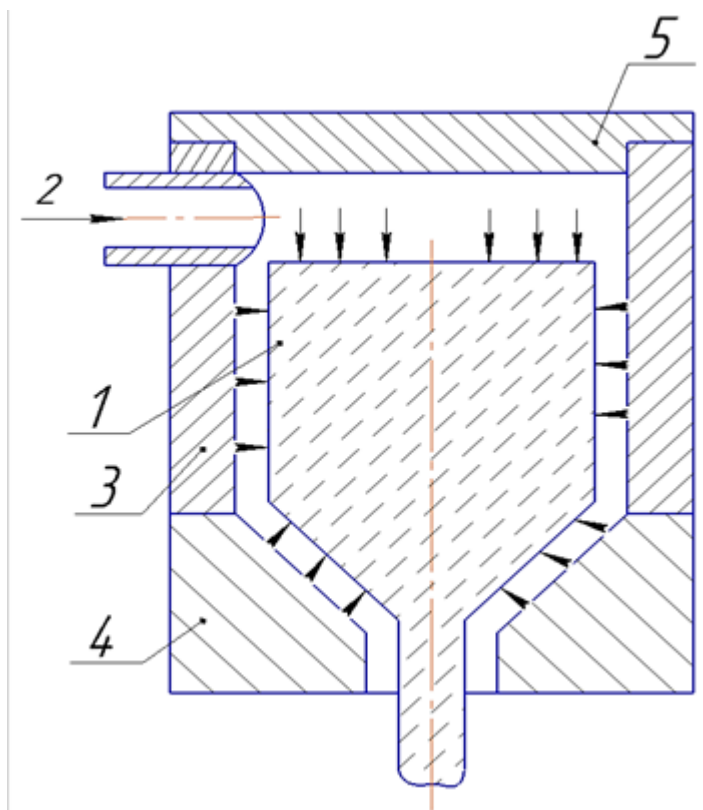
Схема прессования жидкостью высокого давления. 1 - заготовка; 2 - жидкость высокого давления; 3 - контейнер; 4 - матрица.
